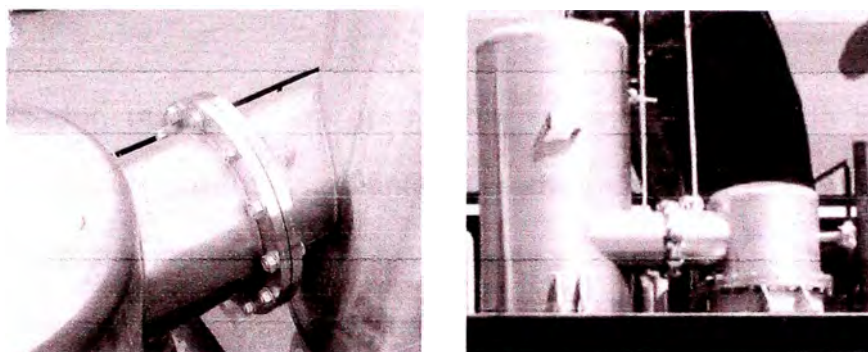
Separador soldado a la estructura
